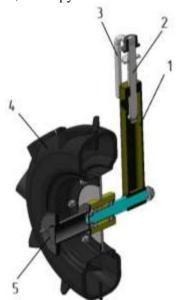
Колесо приводное 1 — стойка; 2 — винт регулировочный; 3 - рукоятка; 4 — диск с шиной (шина 5х10); 5 — приводная звездочка.
